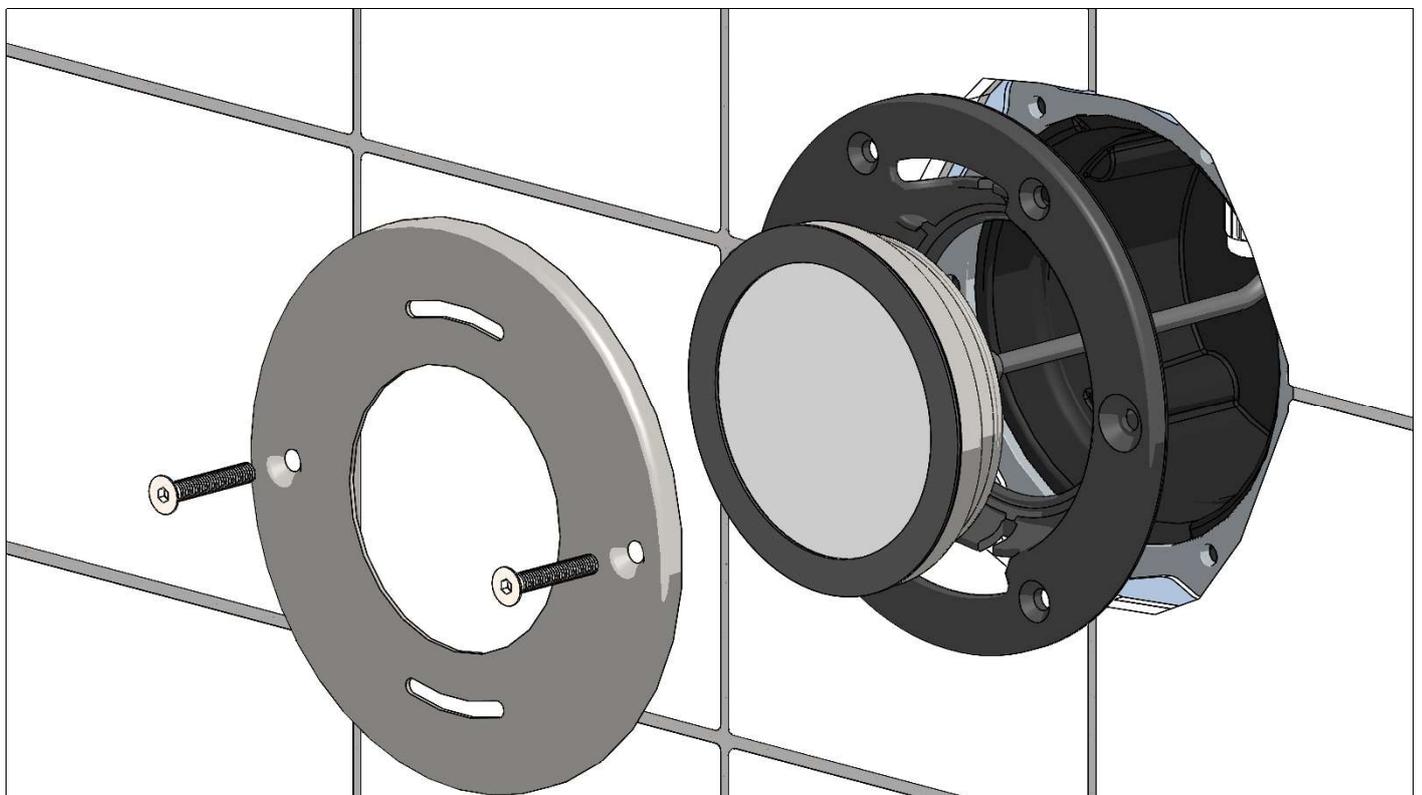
Fertigmontage Betonbecken (gefliest – mit und ohne Flüssigabdichtung)
